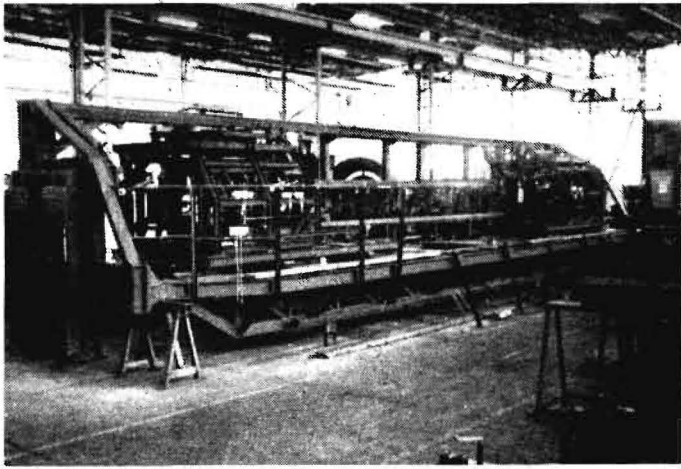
Großschweißvorrichtung mit Elektro-Programmsteuerung für den Schneidwerktrög des Mährescher E 516.
